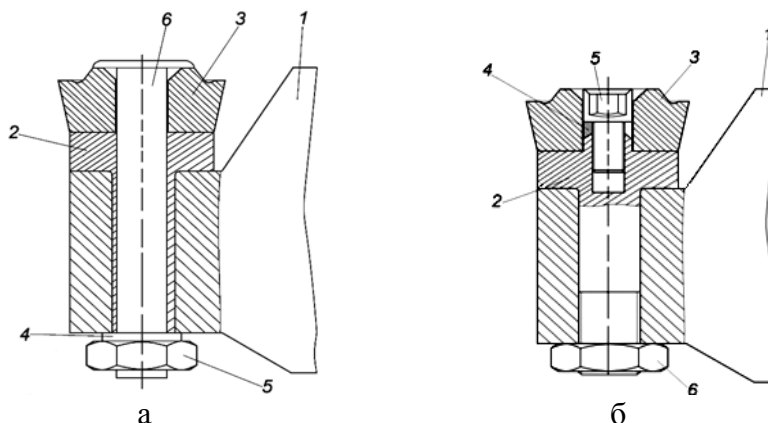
Базовая (а) и усовершенствованная (б) конструкции сборного чашечного резца
